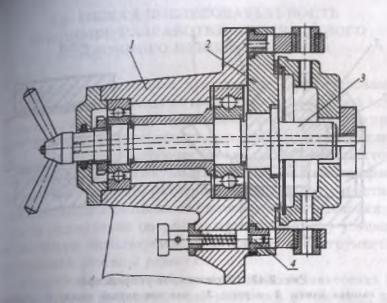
Делительное устройство приспособления: 1 - корпус; 2 - делительный диск; 3 - вал; 4 - фиксатор
